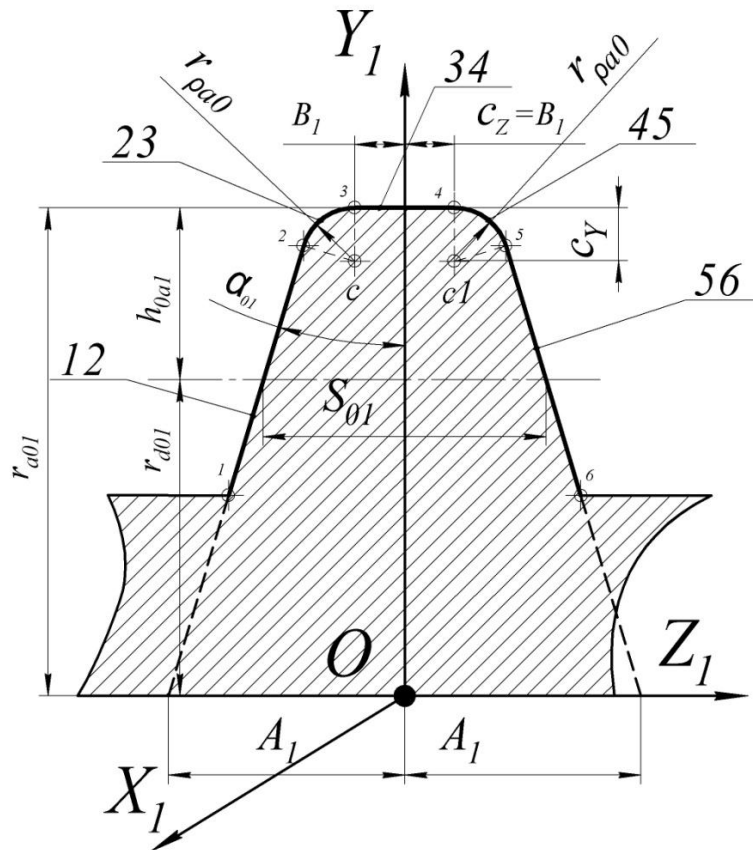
Твірний профіль вихідної інструментальної поверхні стандартної черв'ячної фрези
